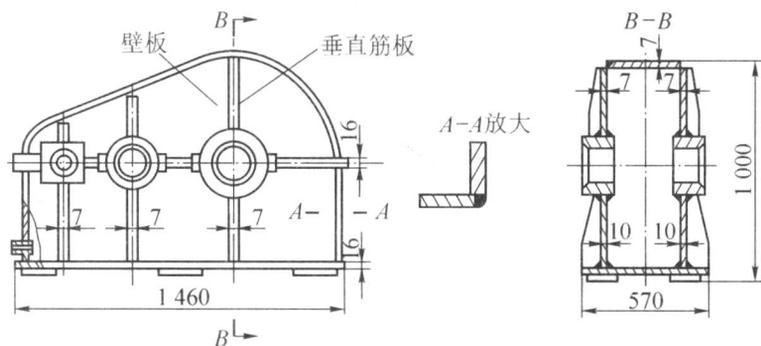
一个单壁剖分式减速器箱体焊接结构
